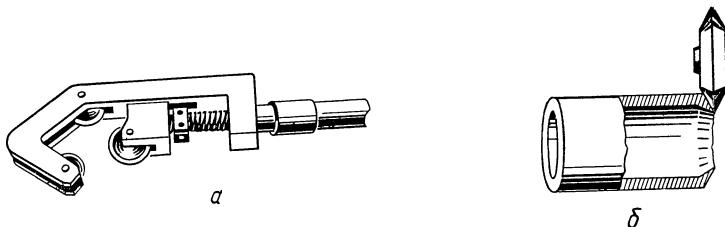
Труборез: *а* — общий вид; *б* — отрезка трубы.
